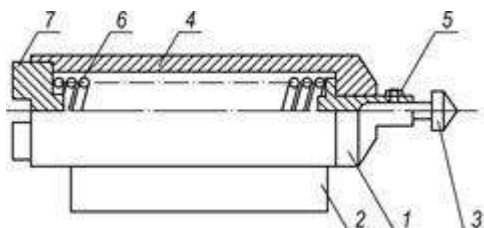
Пристосування для нанесення регулярного мікрорельєфу на бічну поверхню голки розпилювача дизельної форсунки
